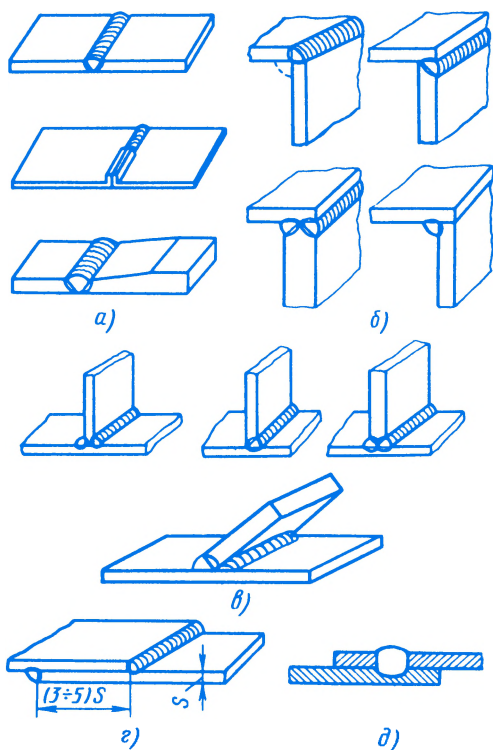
Основные типы сварных соединений: а – стыковые, б – угловые, в – тавровые, г – нахлесточное, д – нахлесточное точечное
